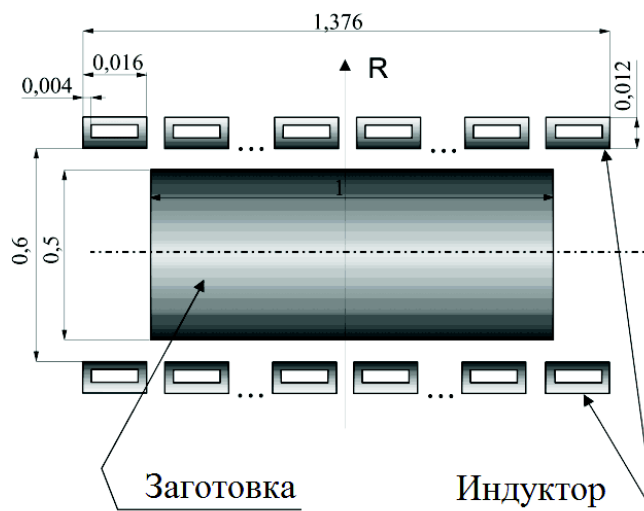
Геометрические параметры системы «индуктор – заготовка»
